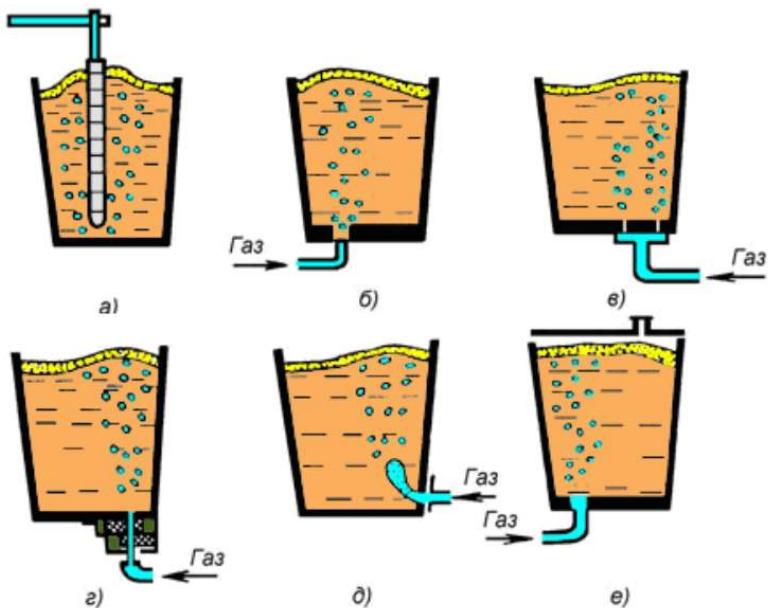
Способы продувки металла в ковше: а – через погружаемую форму; б – через пористый блок; в – через пористые швы в днище; г – через шиберный затвор; д – через боковую стенку ковша; е – способ SAB
